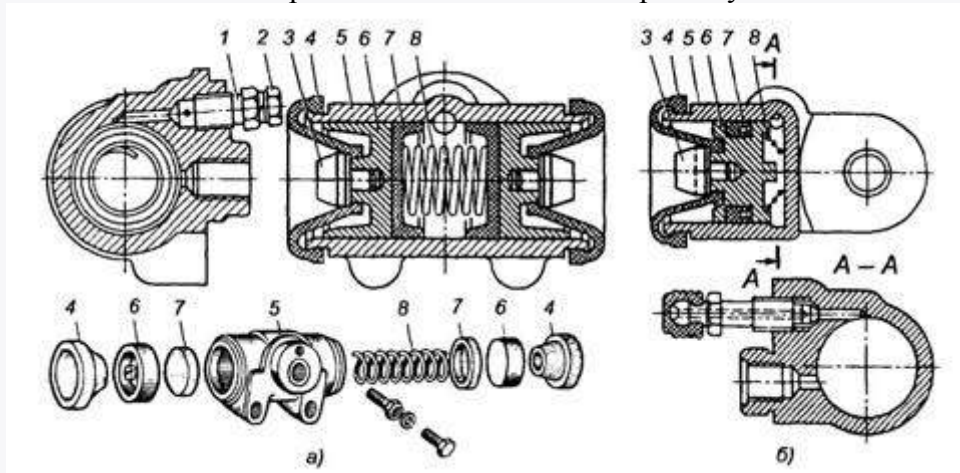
Колесные цилиндры гидропривода тормозных механизмов: а — двух поршневой; б — одно поршневой; 1 — перепускной клапан; 2 — пробка; 3 — толкатель; 4 — резиновый чехол; 5 — корпус цилиндра; 6 — поршень; 7 — резиновая манжета; 8 — пружина.
